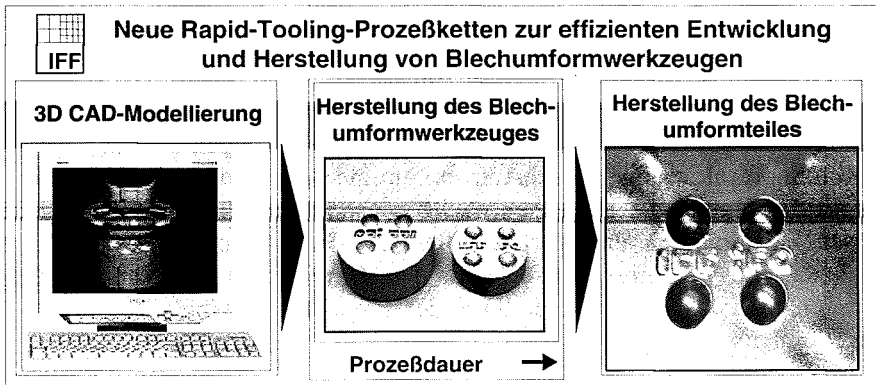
Rapid Tooling für Blechumformwerkzeuge
